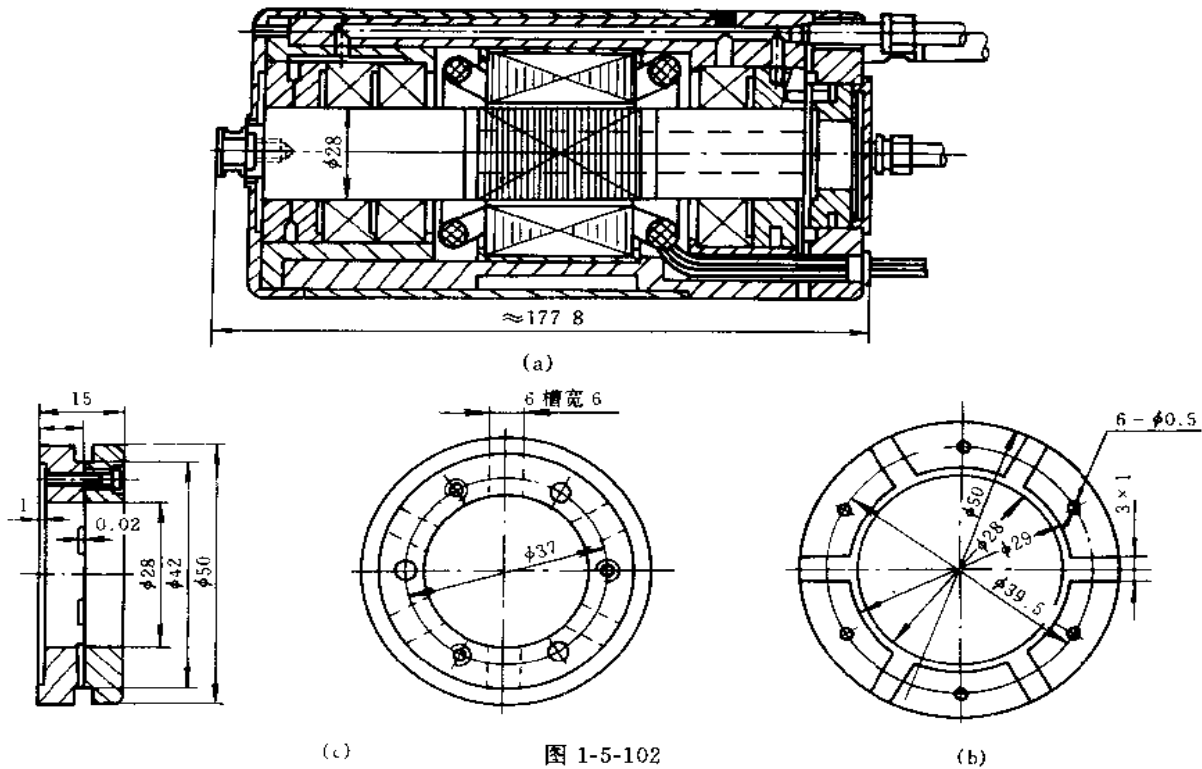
(a) 空气静压电主轴；(b) 推力轴承结构；(c) 径向轴承结构
